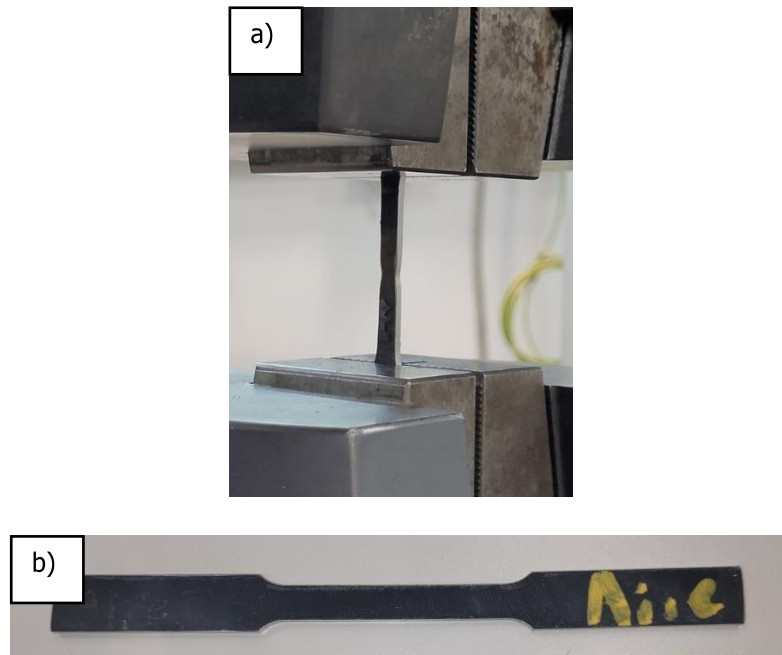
a) probeta montada en la máquina de pruebas universales. b) probeta utilizada.
